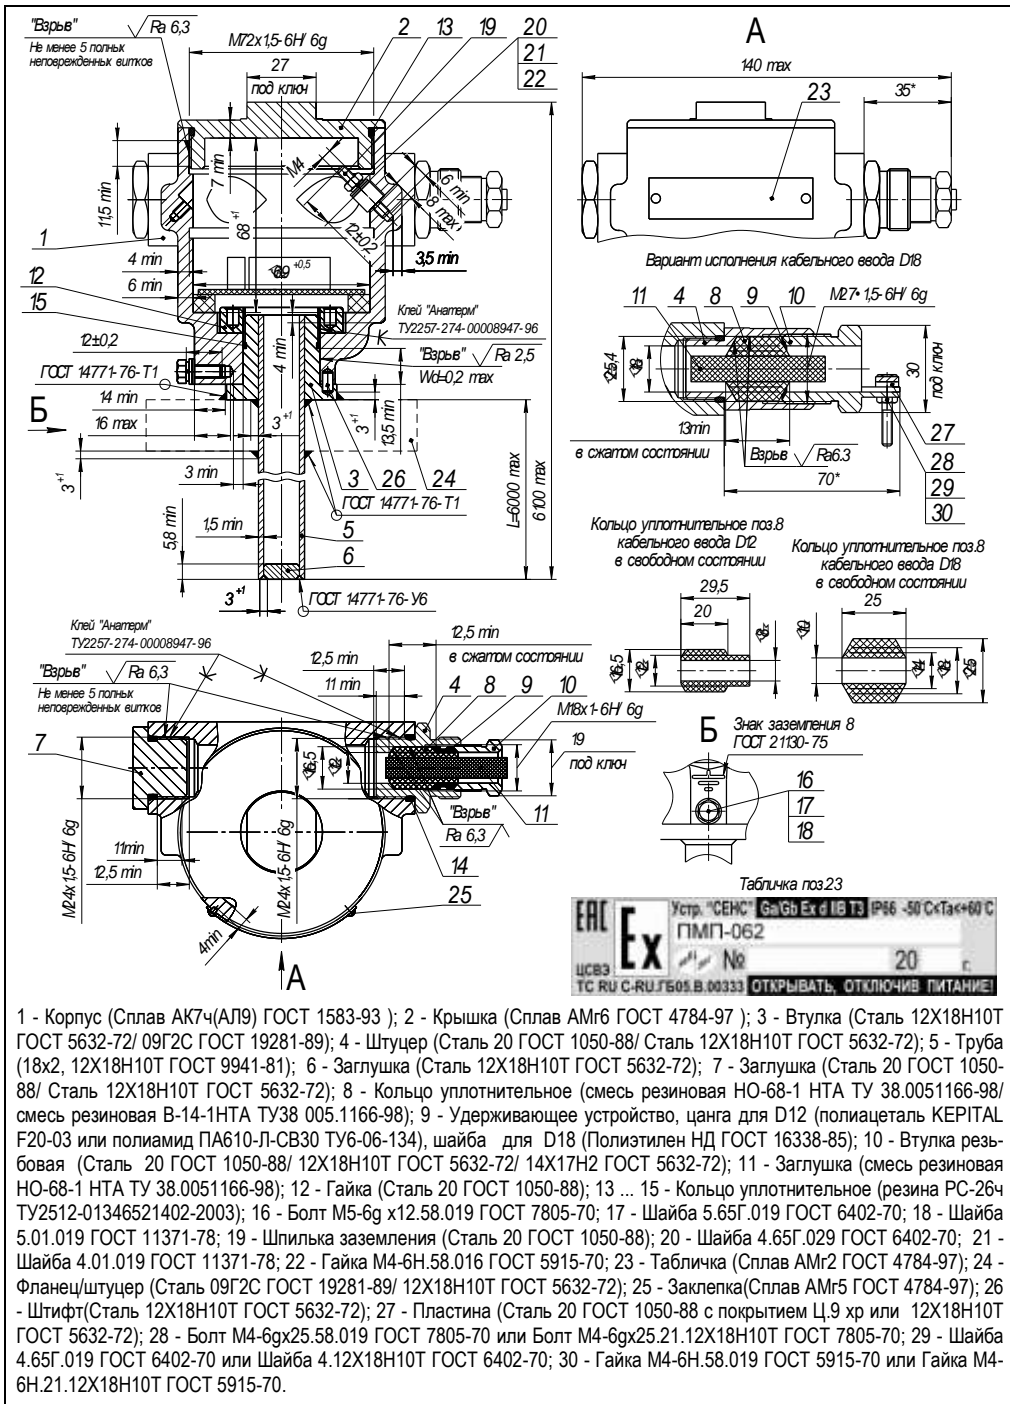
Чертеж средств взрывозащиты для преобразователя с корпусом Л
